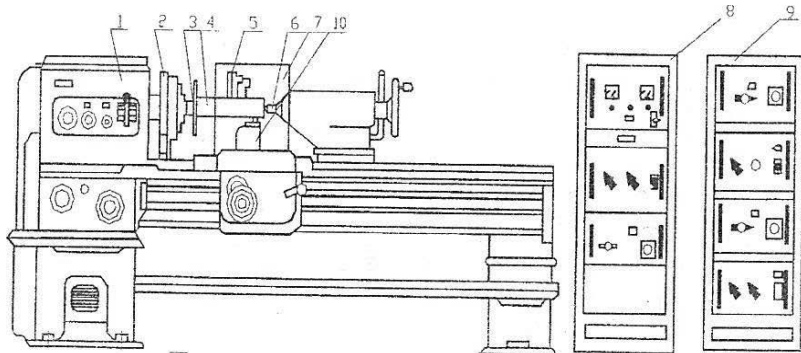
Схема установки «Елітрон-344»: 1 – токарний верстат; 2 – трикулачковий патрон з струмознімачем; 3 – оправка; 4 – оброблювана деталь; 5 – обробна головка; 6 – центр; 7 – екран; 8, 9 – генератори; 10 – обкатник
